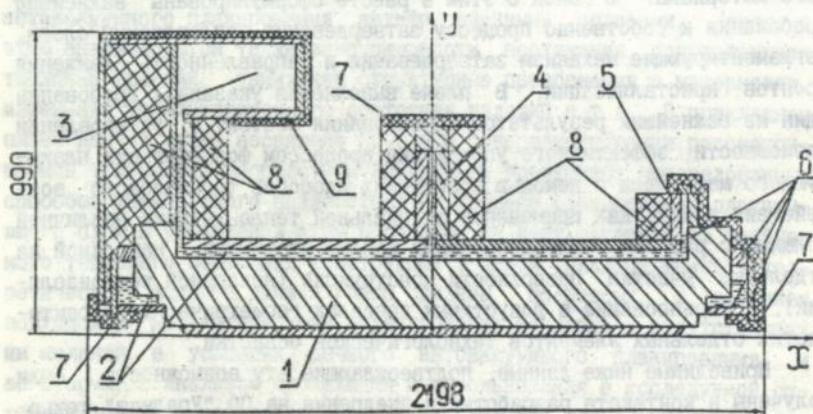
Общий вид скользящей опоры шагающего экскаватора с предлагаемой технологической оснасткой под плакирование: 1 - стальная основа изделия; 2 - наплавочные полости; 3 - коробчатый бункер; 4 - промежуточный питатель; 5 - питатель-газосборник; 6 - контрдетали; 7 - шестислойная изоляция из асбокартона; 8 - изоляция из асбокрошки; 9 - изоляция из асбокартона.
